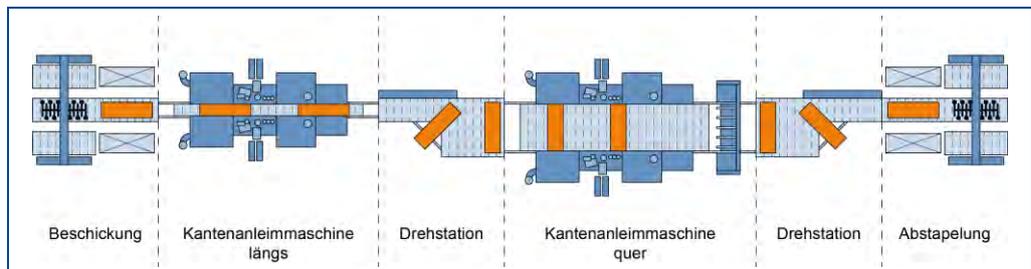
Layout-Zeichnung: Puffer – Beschickung – Längskantenbearbeitung – Drehstation – Querkantenbearbeitung
